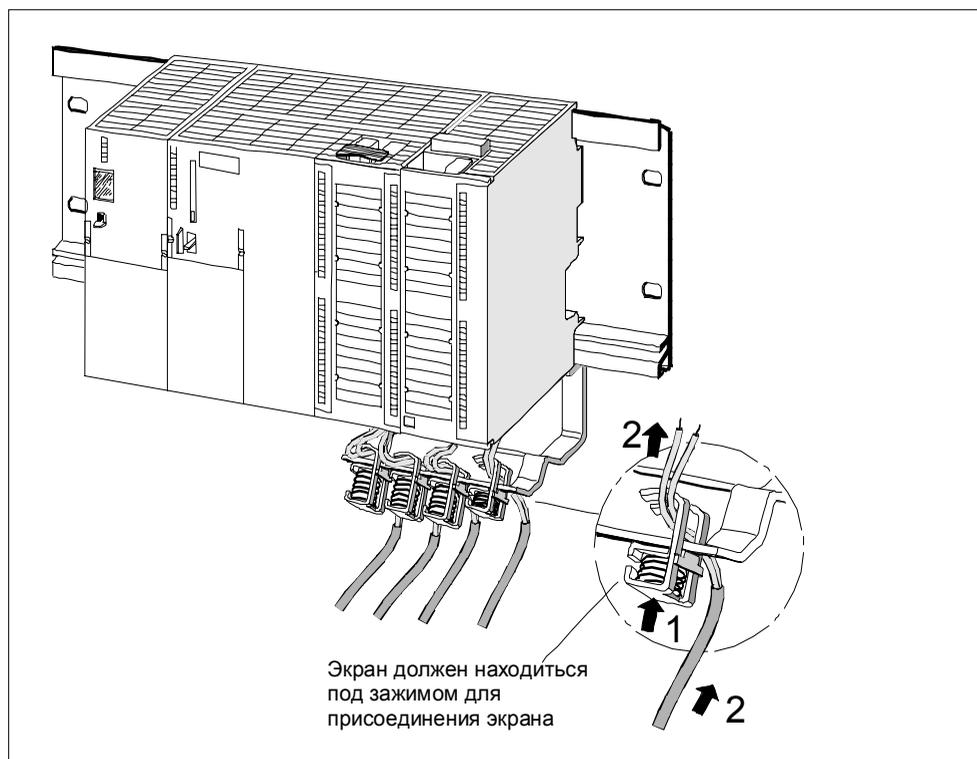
Крепление экранированных двухпроводных линий на опорном элементе для экрана
